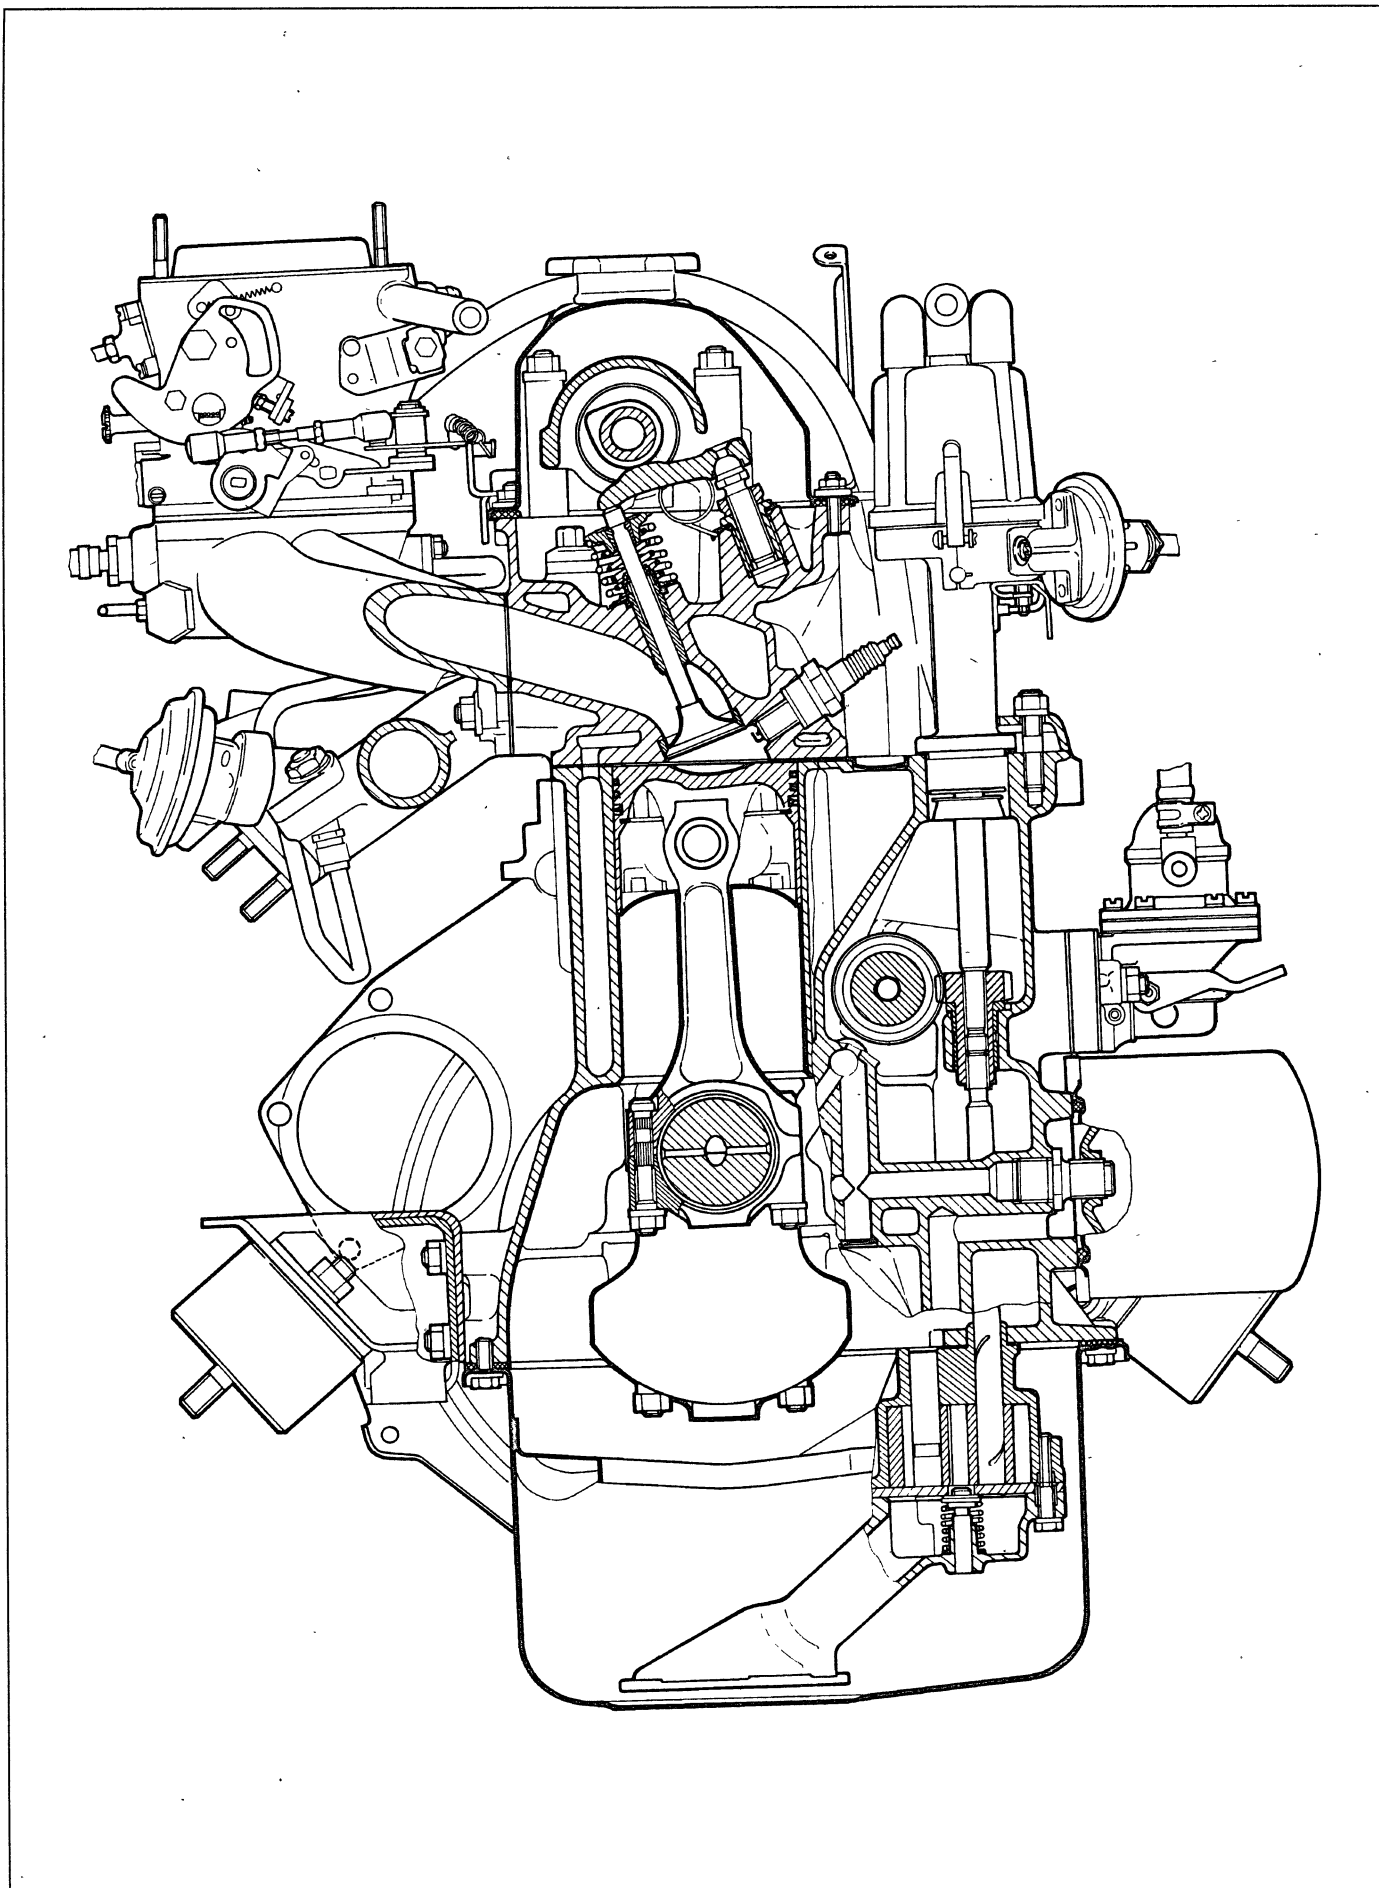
Поперечный разрез двигателя ВАЗ-21213
